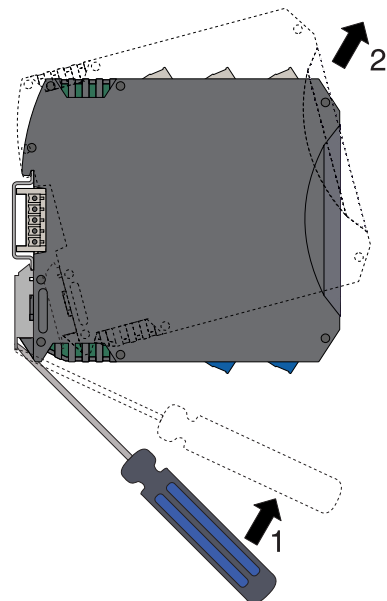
Демонтаж барьера с DIN-рейки
